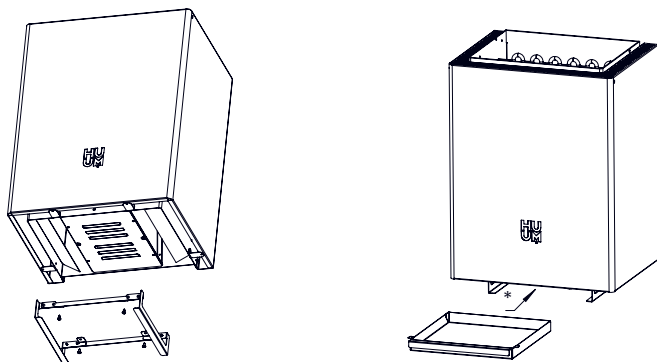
Instaliranje preusmjerivača topline u HUUM CORE Wall i CORE Wall Mini.
